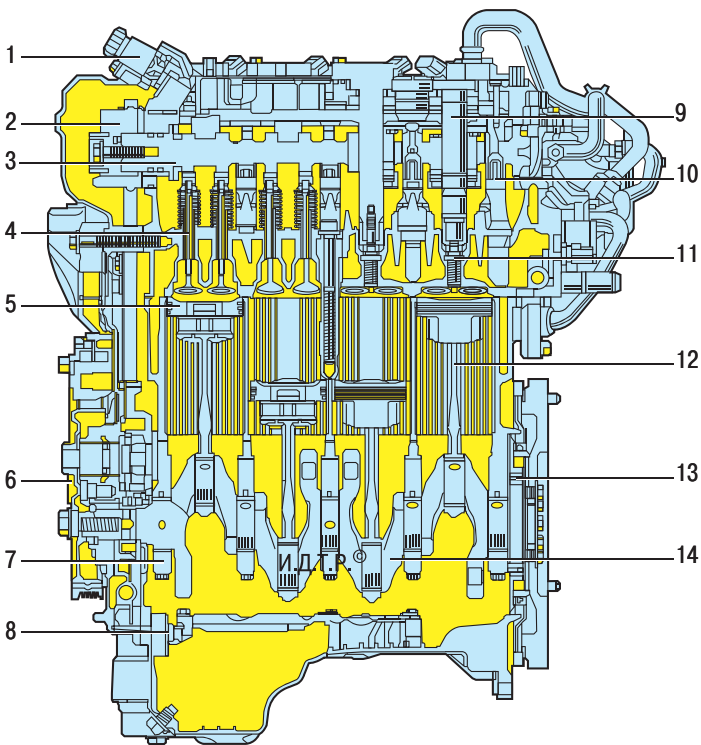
Двигатель 1NR-FE (продольный разрез): 1 – гидравлический клапан изменения фаз газораспределения; 2 – контроллер системы VVT-i; 3 – распределительный вал; 4 – клапан; 5 – поршень; 6 – шкив привода вспомогательных агрегатов; 7 – крышка коренного подшипника; 8 – масляный насос; 9 – катушка зажигания; 10 – постель распределительного вала; 11 – свеча зажигания; 12 – шатун; 13 – задний сальник коленчатого вала; 14 – коленчатый вал
